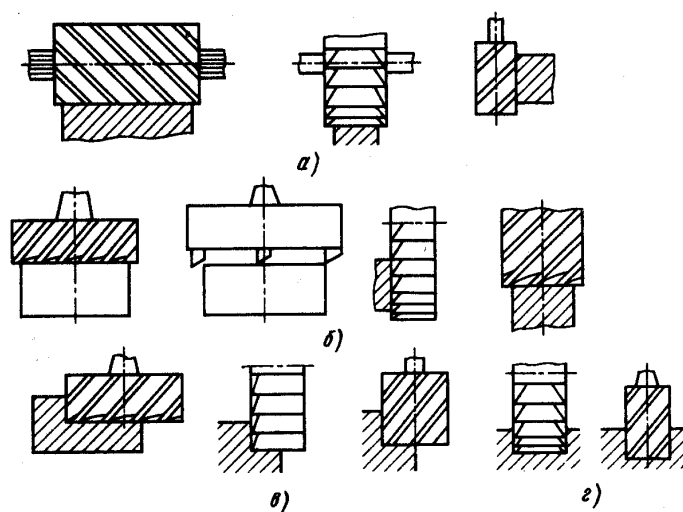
Схемы фрезерования различных плоских поверхностей:
